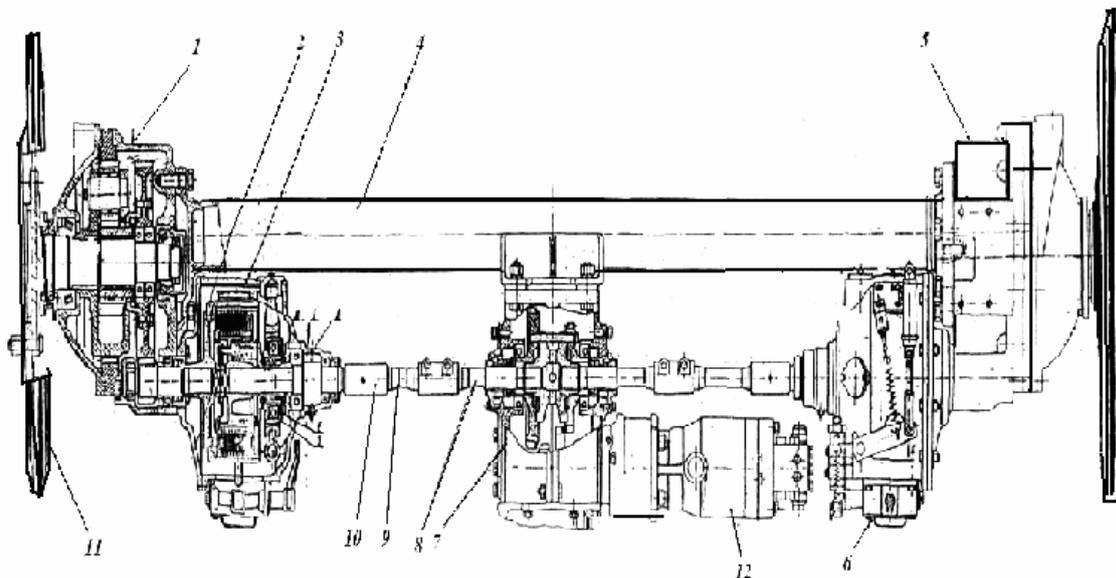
Мост ведущий 1 – редуктор бортовой правый; 2 – барабан со ступицей; 3 – фрикцион бортовой правый; 4 – балка моста ведущего; 5 – редуктор бортовой левый; 6 – фрикцион бортовой левый; 7 – коробка диапазонов; 7 – коробка диапазонов; 8 – полуось правая; 9 – полуось; 10 – втулка соединительная; 11 – звездочка ведущая; 12 – гидромотор
